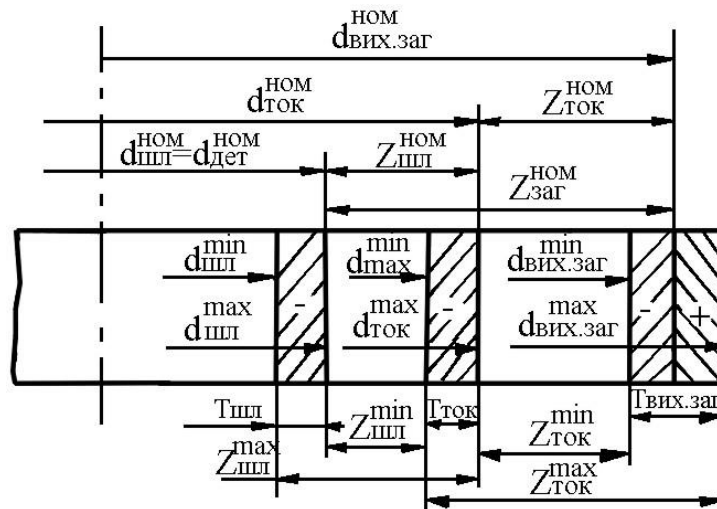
Схема розташування припусків і допусків при токарній обробці та шліфуванні валу
